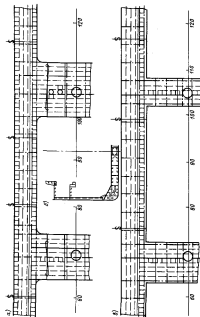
Конструкция судна с широкими распорными палубами и распорными палубами: а - главный палуба; б - вторичная палуба
